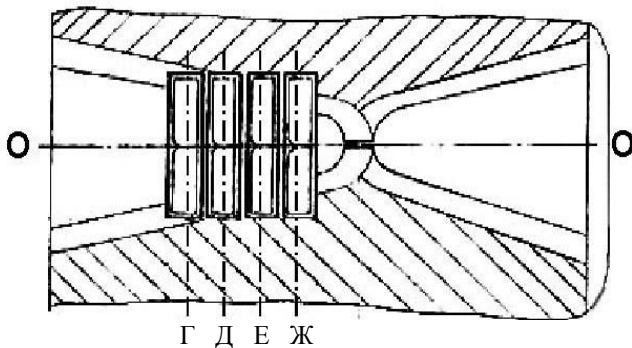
Схема вирізки ЗС типу "Ш" і "С" з металу зварного шва.
